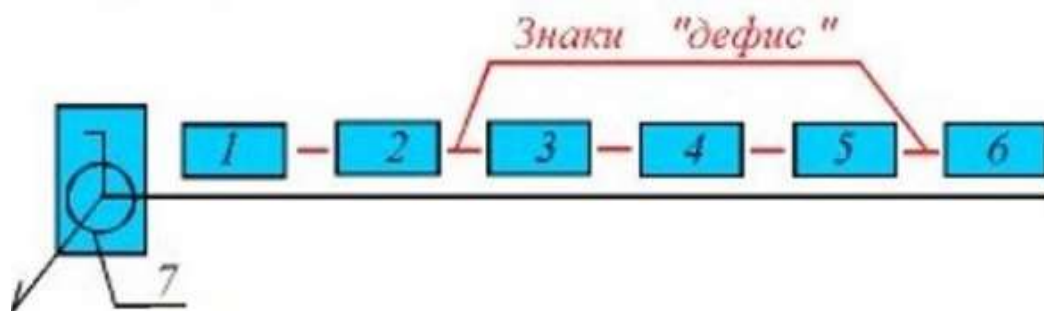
Структура условного обозначения сварного шва
